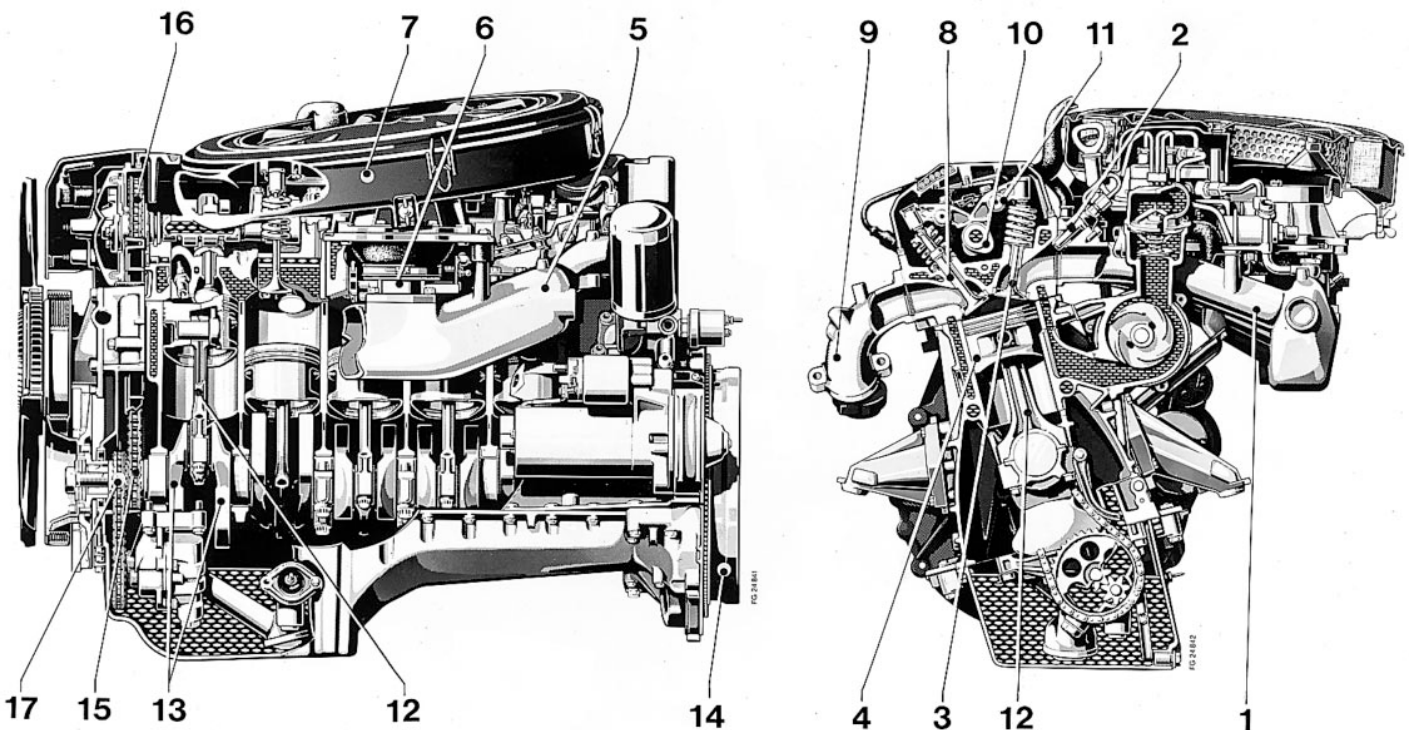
Längs- und Querschnitt des Sechszylinder-Motors M103 (300E)
